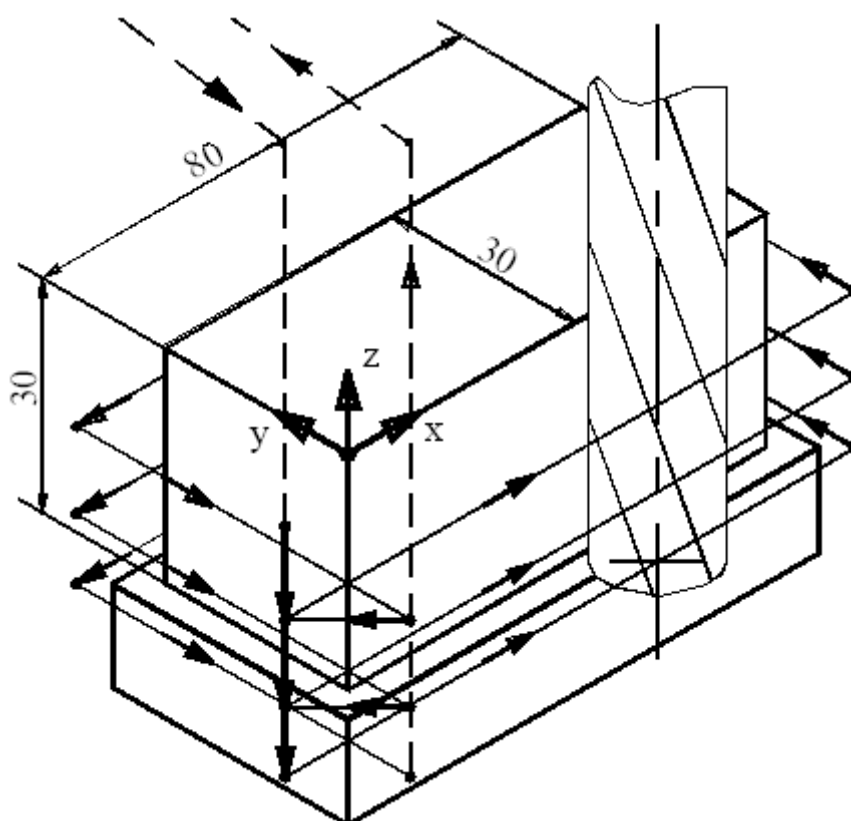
Обработка детали и траектории движения инструментов по контуру
